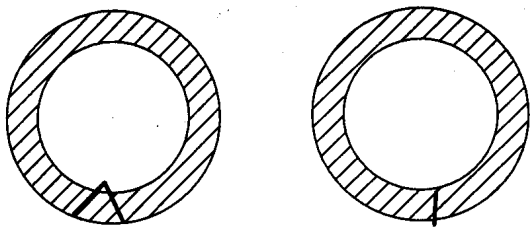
矩形坯对接后焊缝形状 图 4 梯形坯料对接后焊缝形状
